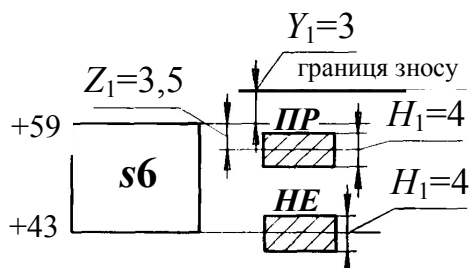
Схема полів допусків вала і калібрів для його контролю
